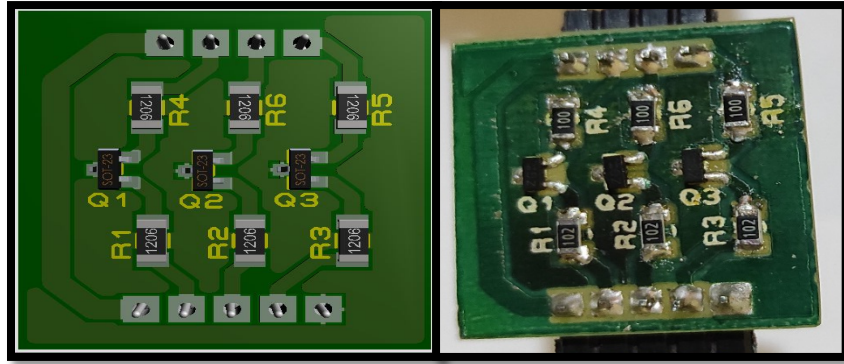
Diseño PCB del lado TOP del interruptor lógico.
